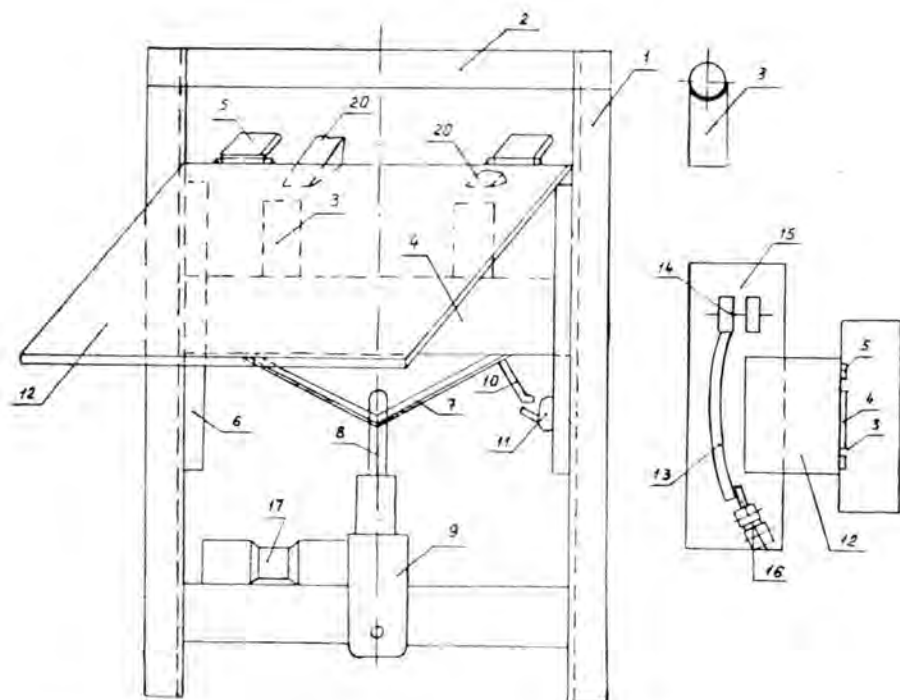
Схема шиберного бункерно-загрузочного устройства и направления детали в загрузочную зону шлифовальной линии.
